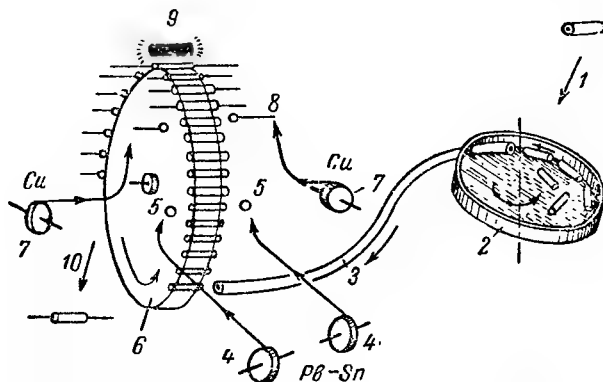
Схема автомата для пайки выводов к трубчатым заготовкам при изготовлении конденсаторов типа КТК.
